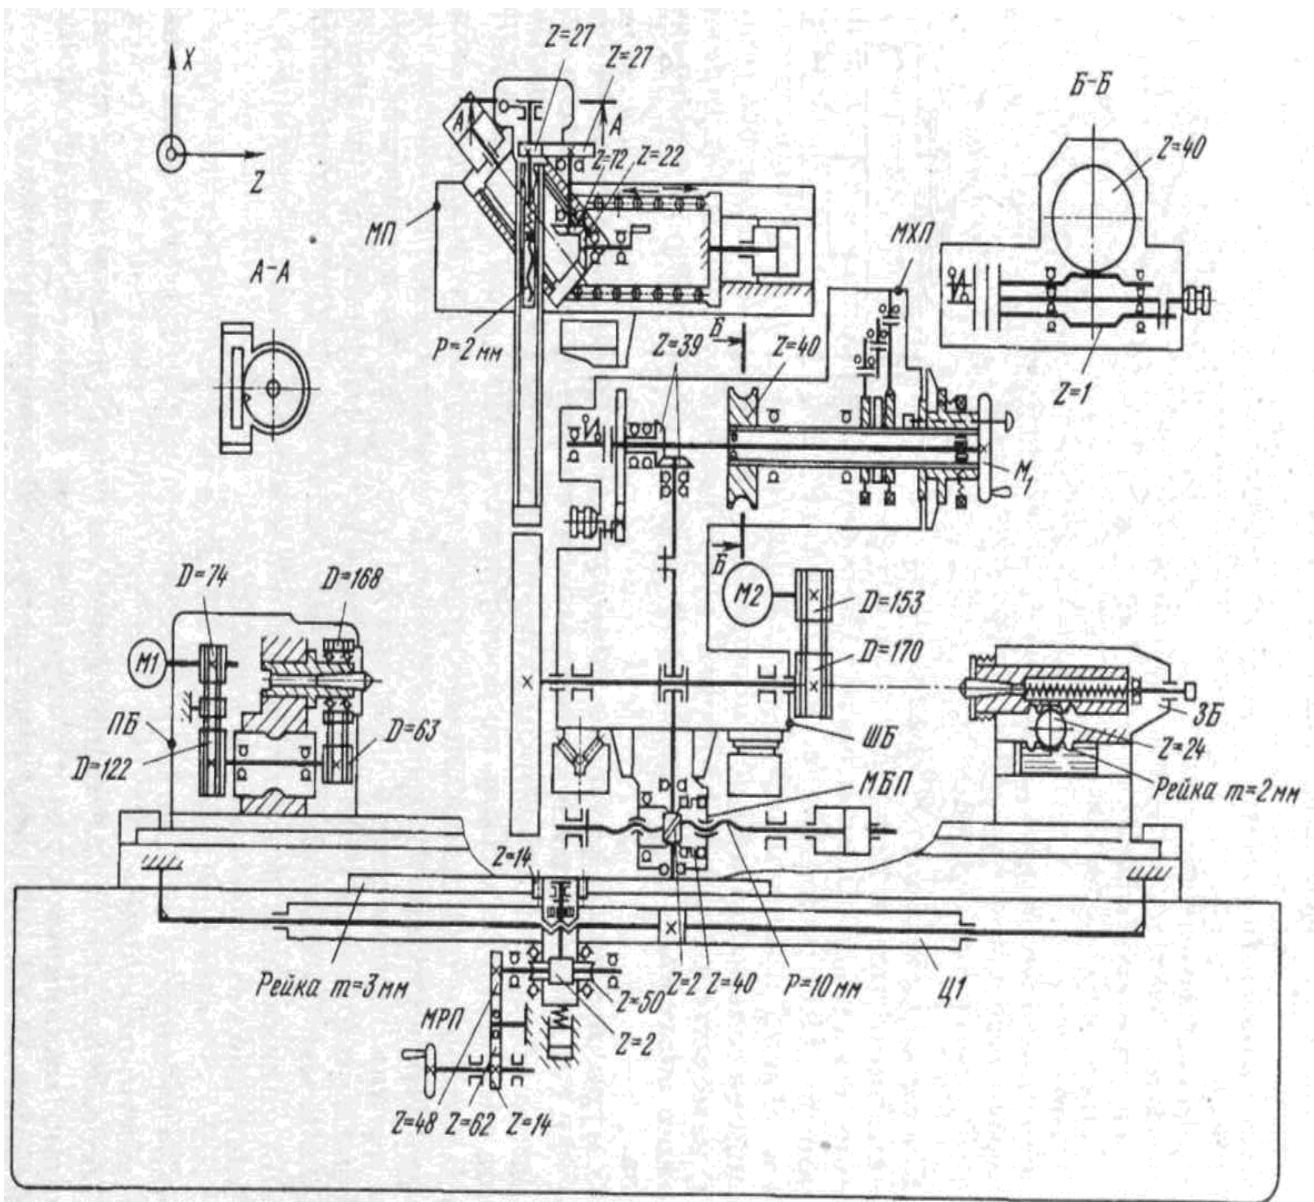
Кинематическая схема круглошлифовального станка.
